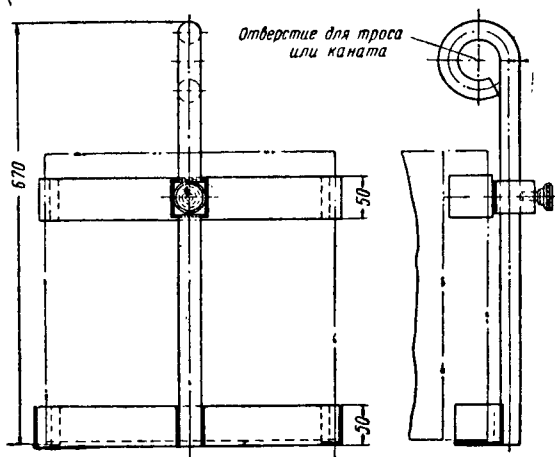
Приспособление для снятия главных полюсов тягового двигателя
